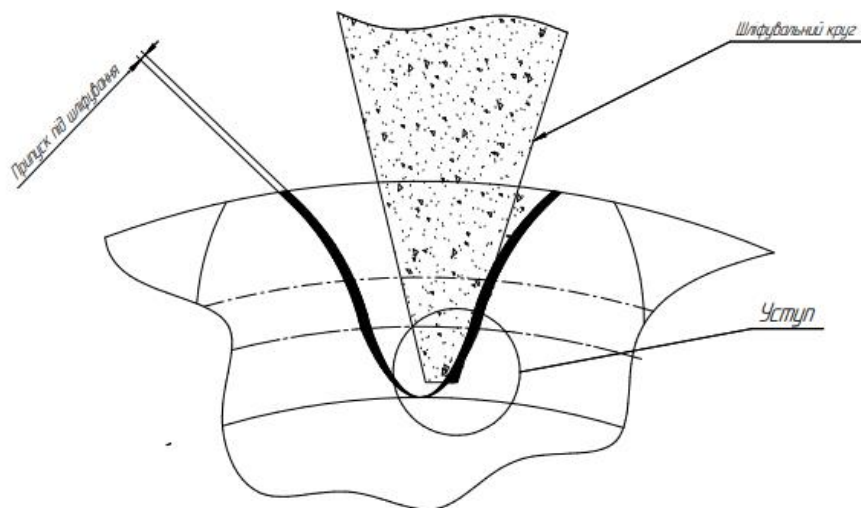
Профіль зубчастого колеса під зубошліфування без піднутрення
